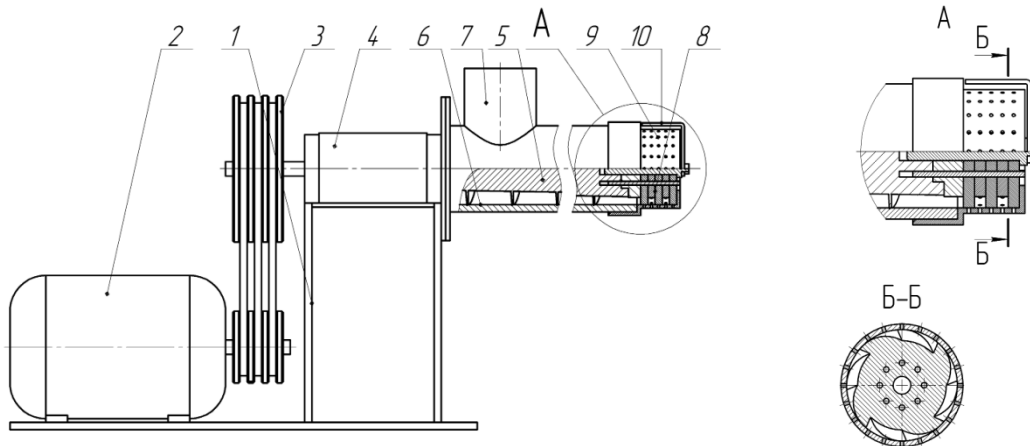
Конструктивно-технологічна схема установки для виготовлення пелет (пелетератора): 1 – рама; 2 – електродвигун; 3 – шків; 4 – підшипниковий вузол; 5 – гвинт; 6 – циліндричний корпус; 7 – завантажувальний бункер; 8 – формуючий кулачок; 9 – циліндрична матриця; 10 – ніж
